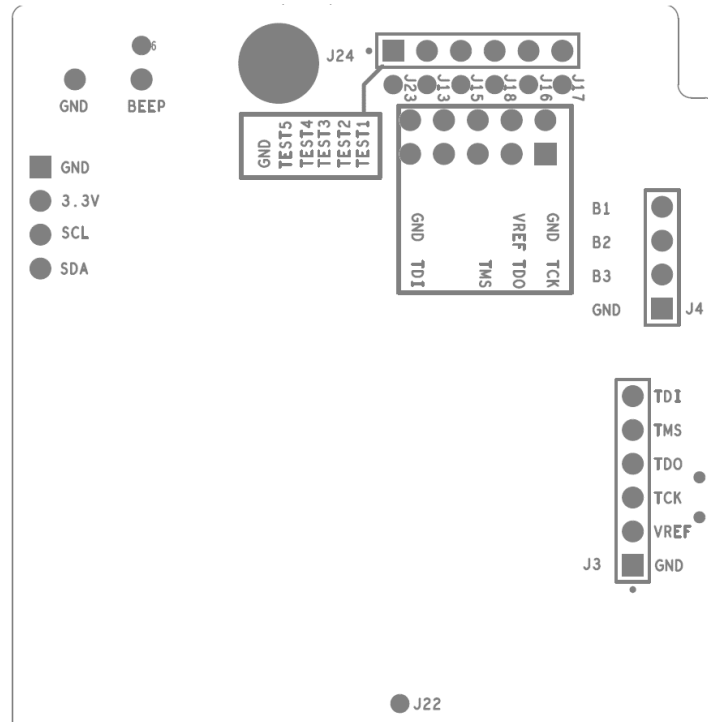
AL-LINK-PRO 离线下载器内部 PCB 板背面丝印
